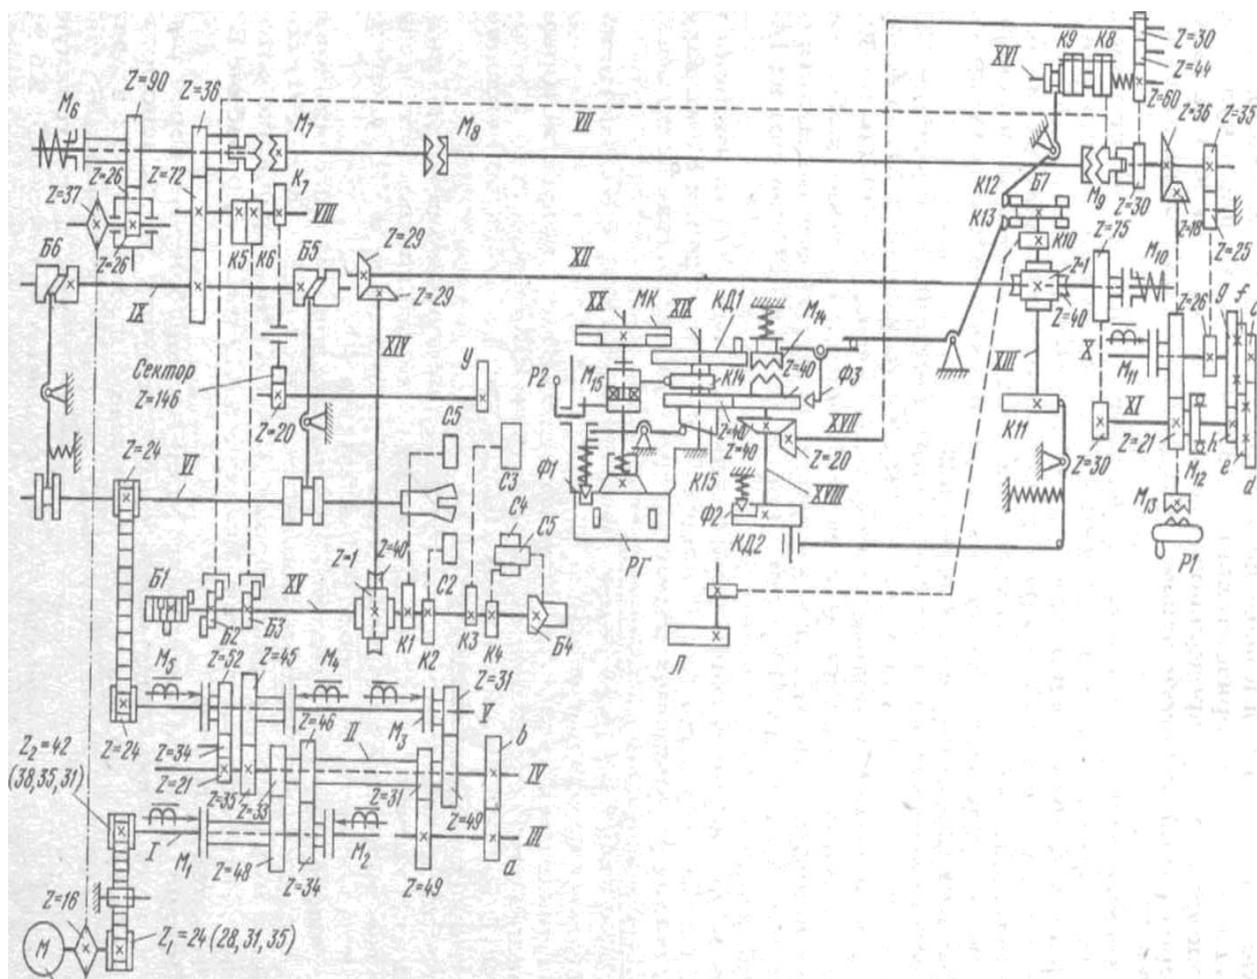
Кинематическая схема токарно-револьверного автомата 1Е140П.
